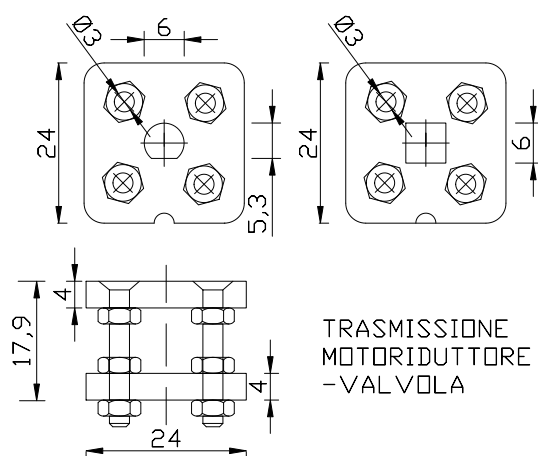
Disegno CAD del sistema di trasmissione motoriduttore-valvola
